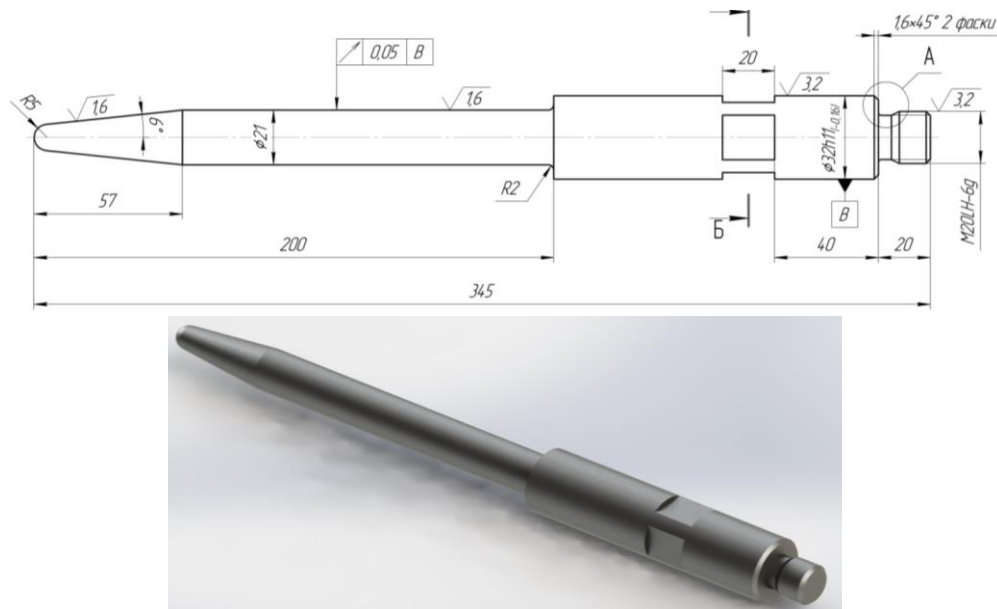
Оправка с оправочным стержнем прошивного стана «30-80» для прошивки заготовки диаметром 31,5 мм
